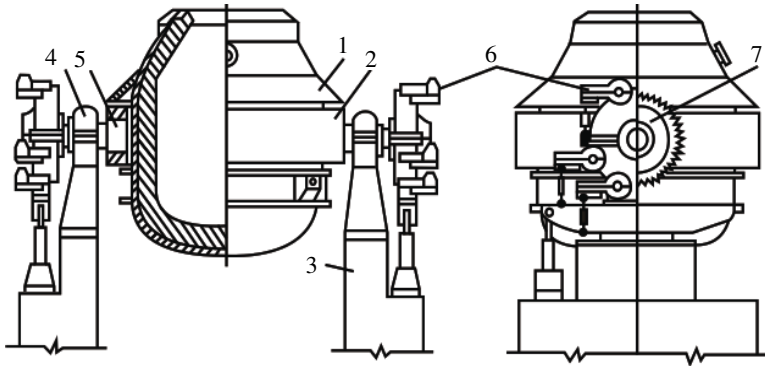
Схема кисневого конвертера: 1 – захисний кожух; 2 – опорне кільце; 3 – опорна станина; 4 – опорний підшипник; 5 – цапфа; 6 – навісний електродвигун із редуктором; 7 – ведене зубчасте колесо
